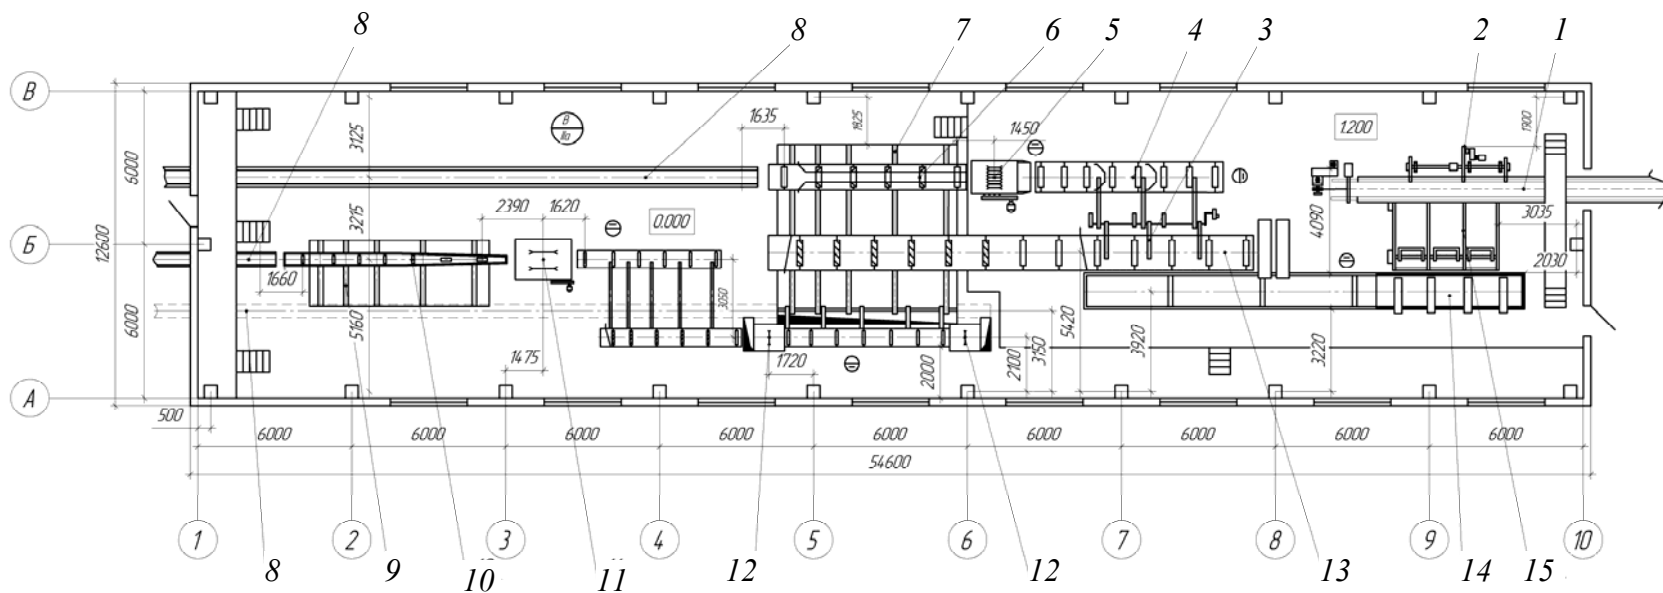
Схема расположения оборудования в цехе на базе вертикального ленточнопильного и круглопильного станков:
